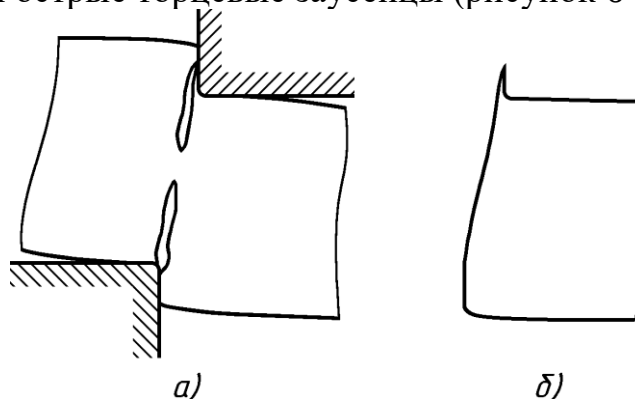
Разделение материала с притупленной режущей кромкой (а) и образование торцевого заусенца (б)
